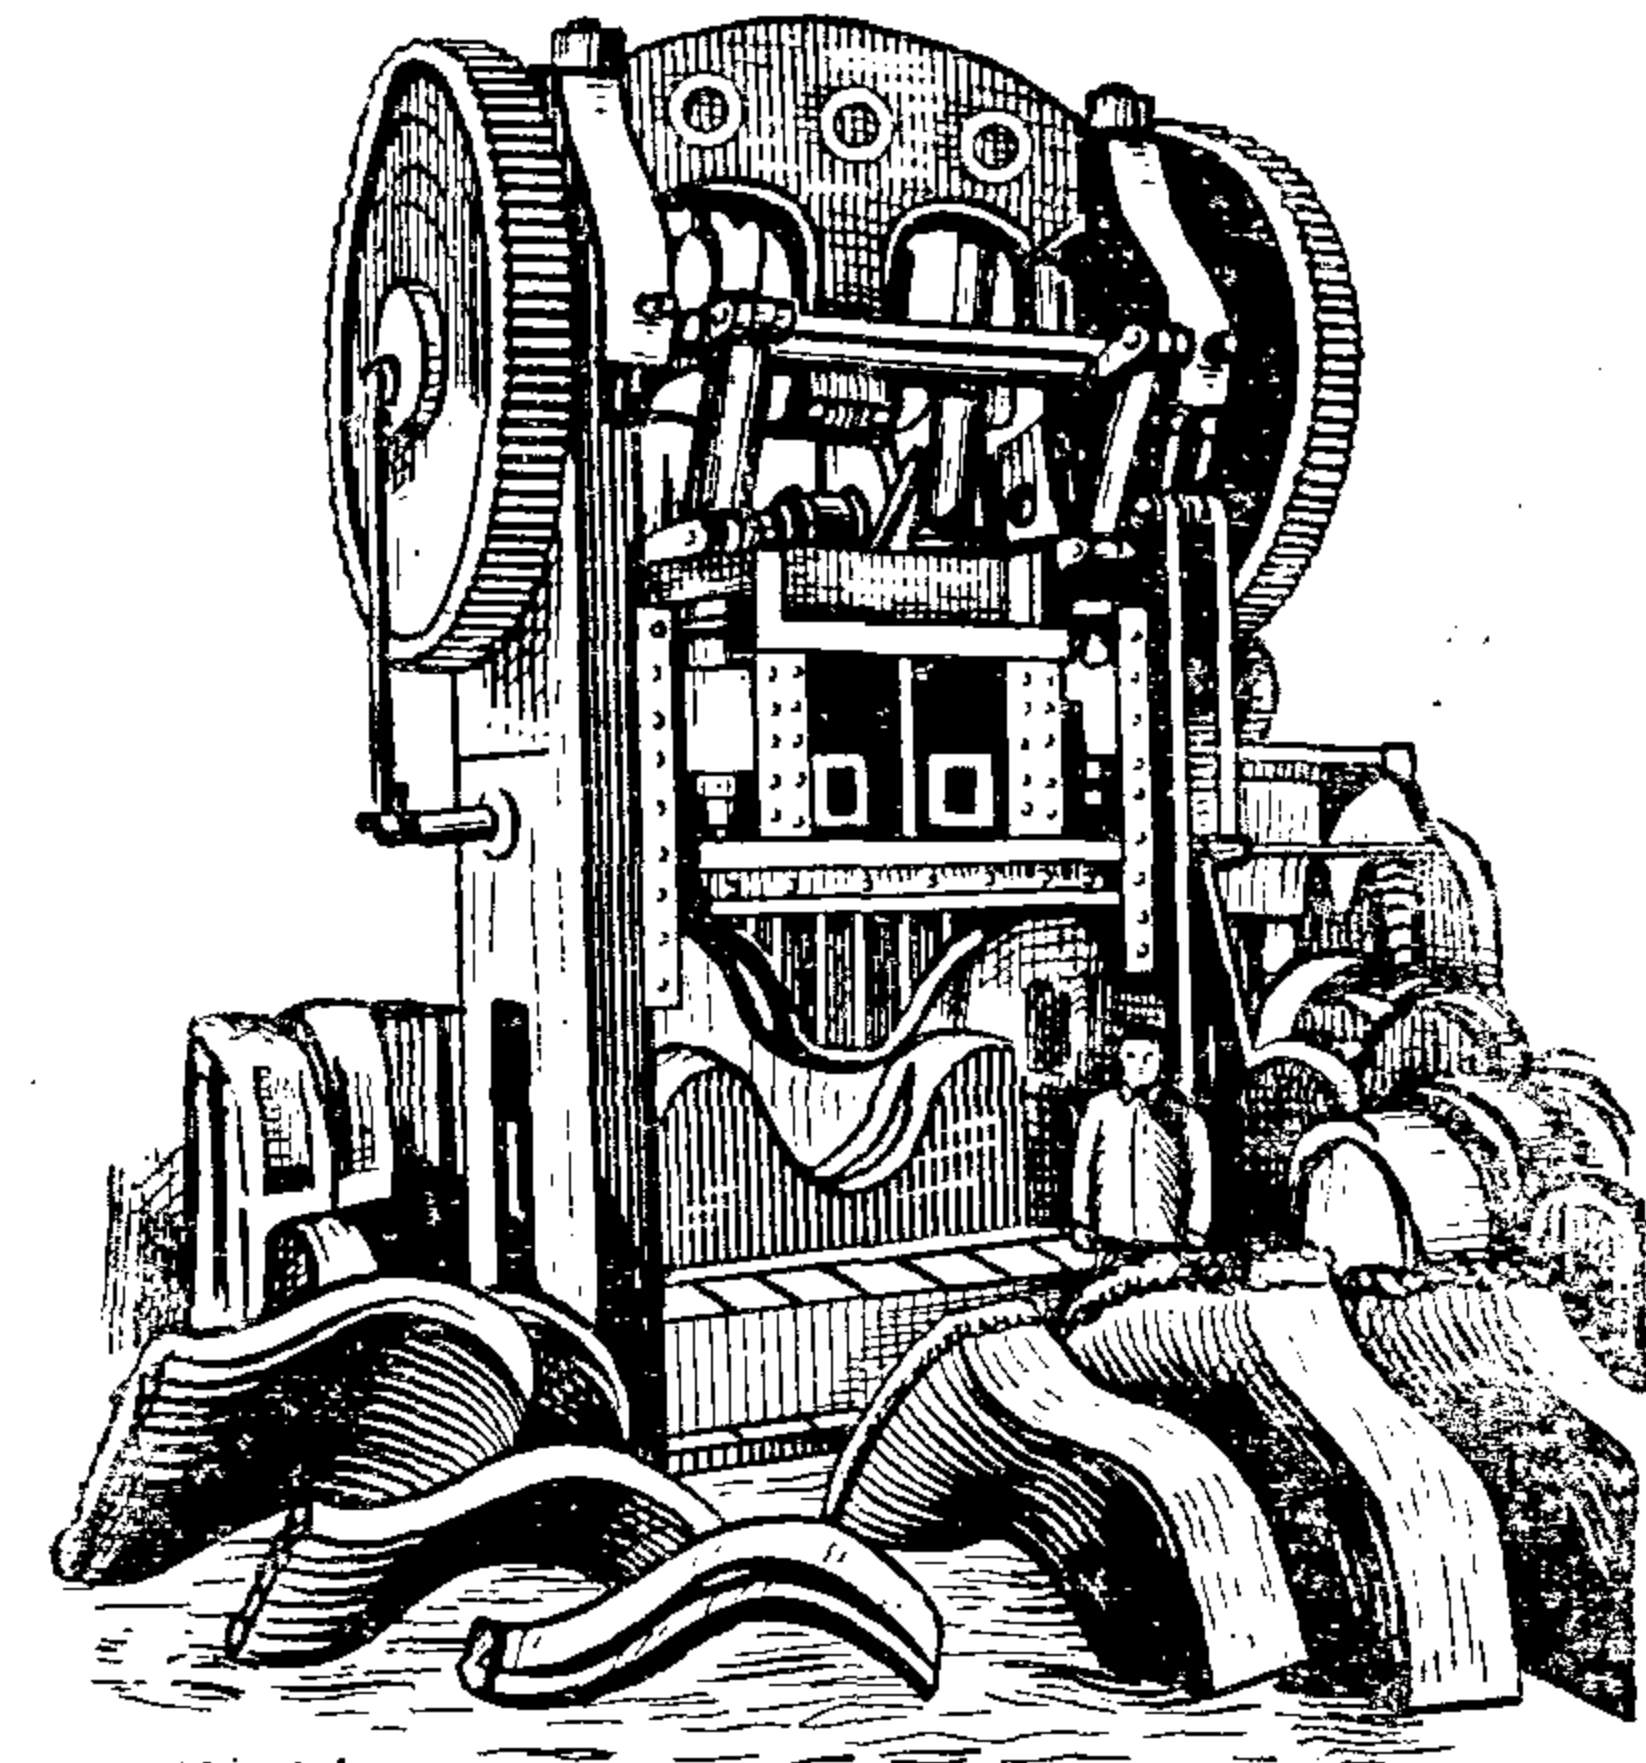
Коленчато-рычажной пресс с пневматической подушкой для выталкивания изделий
